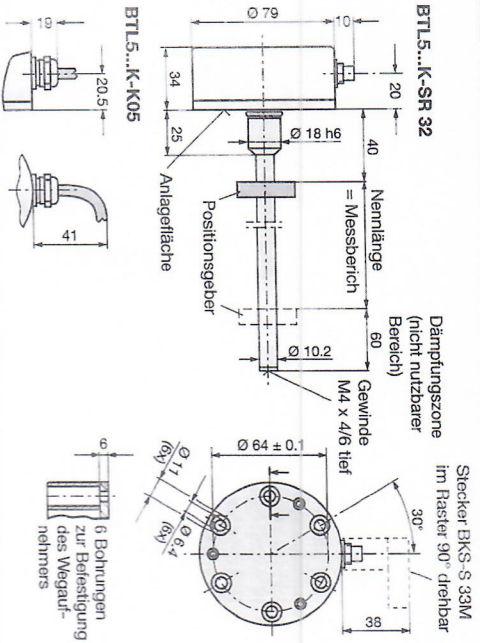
Wegaufnehmer BTL5...K... Maßzeichnung
